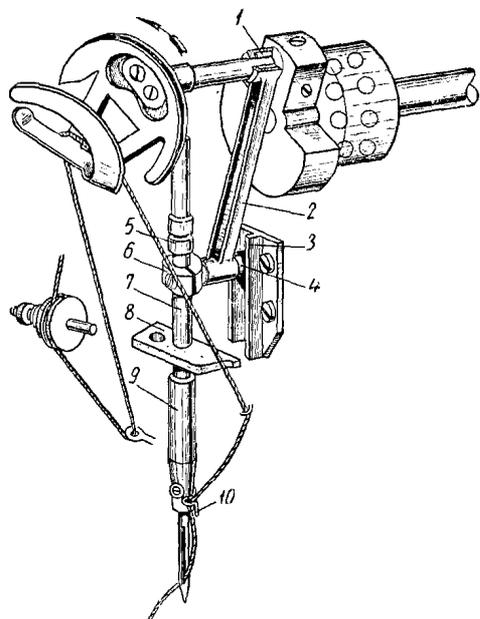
Механизм иглы машины 97-го класса ПМЗ
